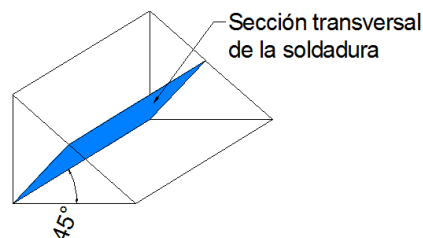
41 - Área de cálculo de la soldadura
